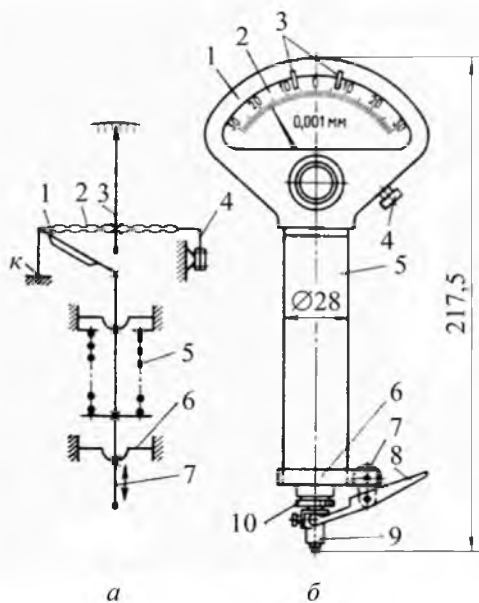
Пружинная измерительная головка ИГП – микрокатор: а – схема; б – внешний вид
